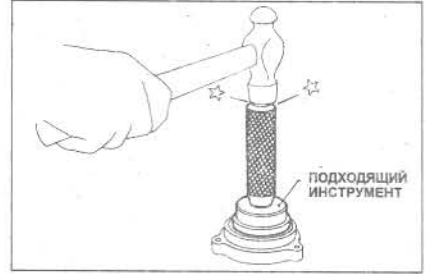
Вбивание подшипника держателя в кожух - инструмент должен прилагаться только к наружному кольцу подшипника (Глава 4)
